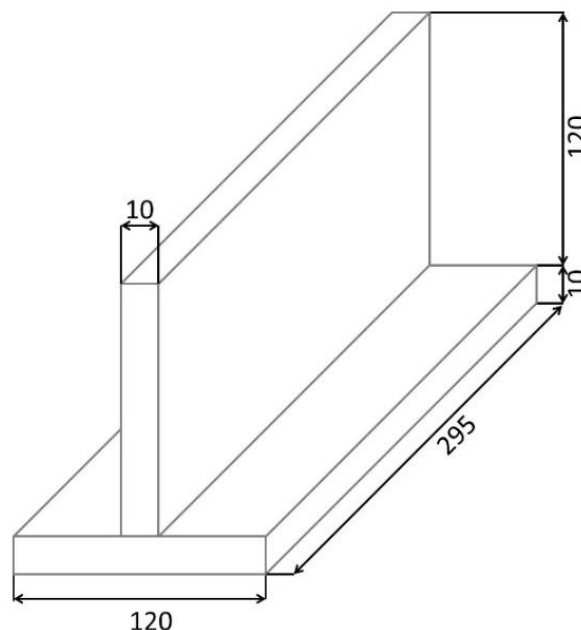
Representação dos corpos de prova soldados usando chapas do aço ASTM A572 GR50 (Dimensões em mm).
